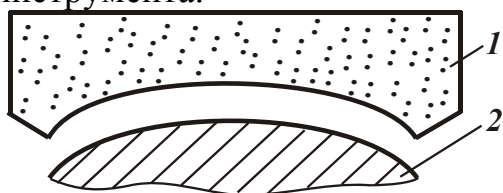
Шлифование выпуклых сферических поверхностей: 1 – шлифовальный круг; 2 – обрабатываемая деталь.
